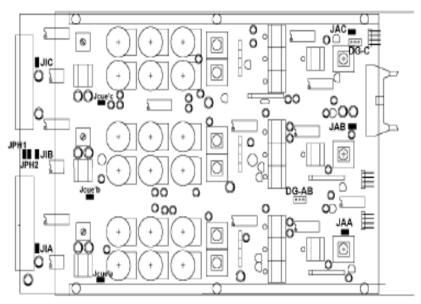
Módulo de micrófono 2812 (vista lado soldaduras)
